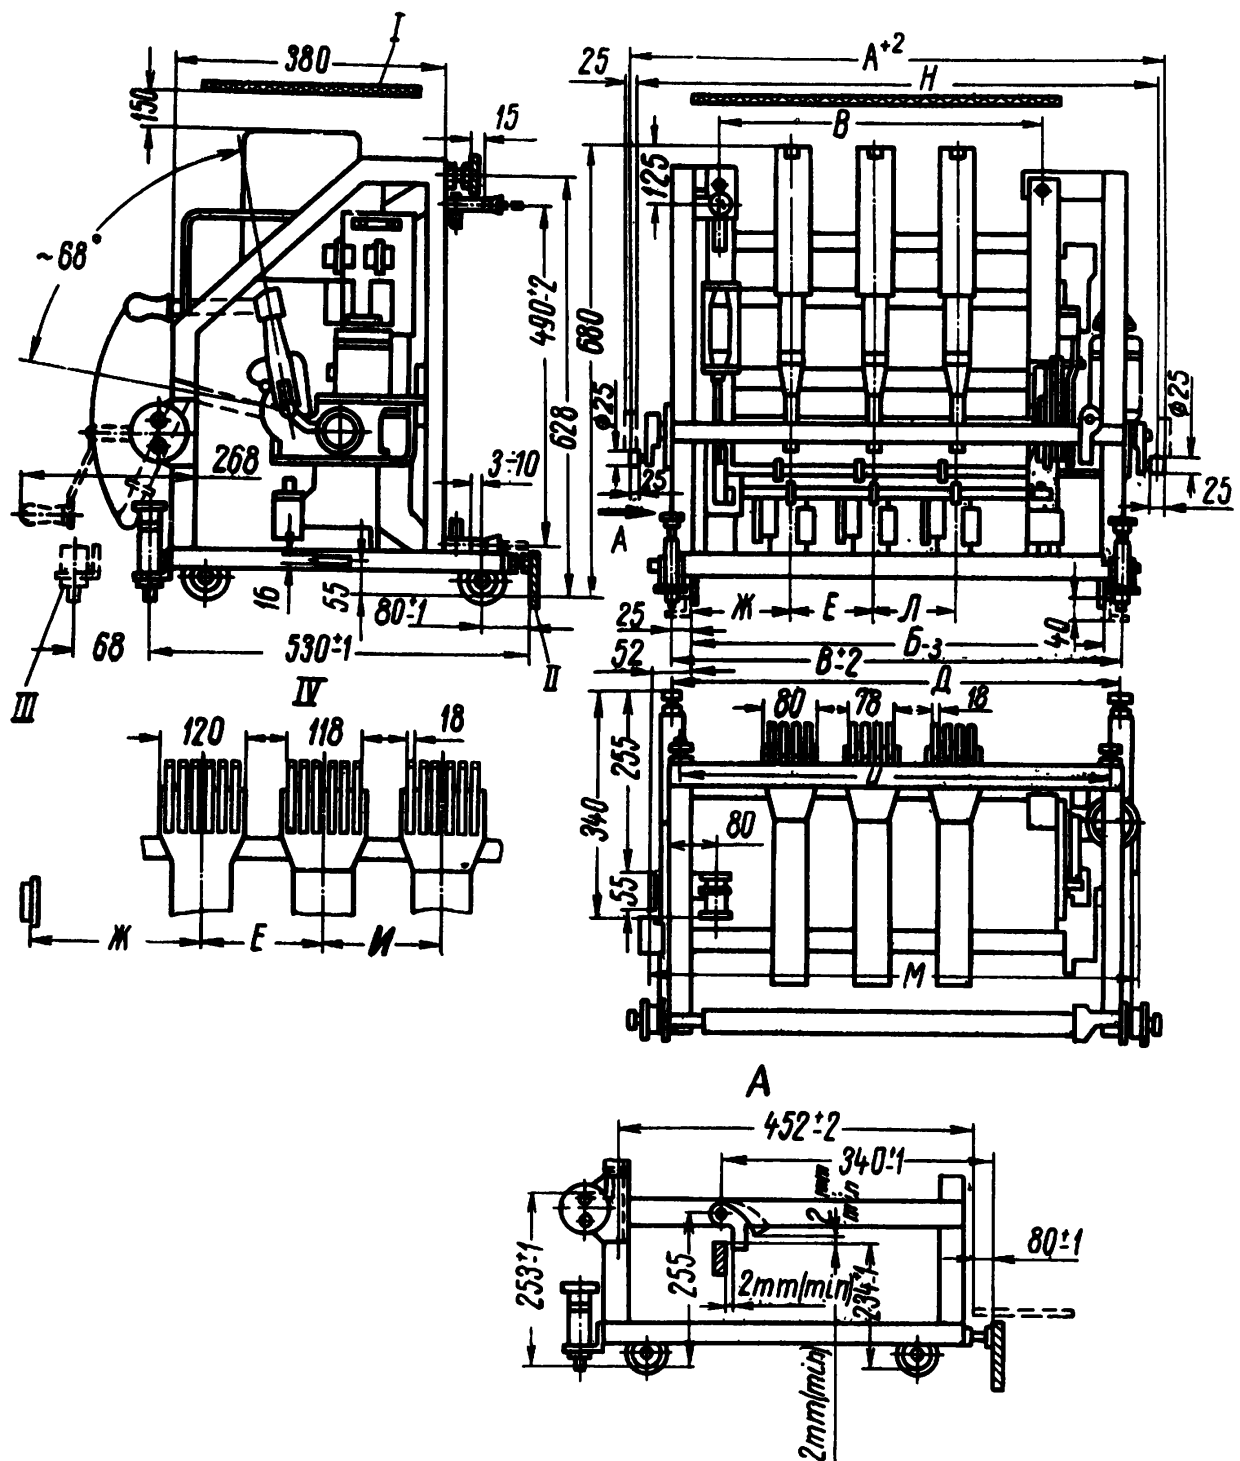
Габаритно-установочные размеры выдвижных выключателей с электродвигательным приводом:
